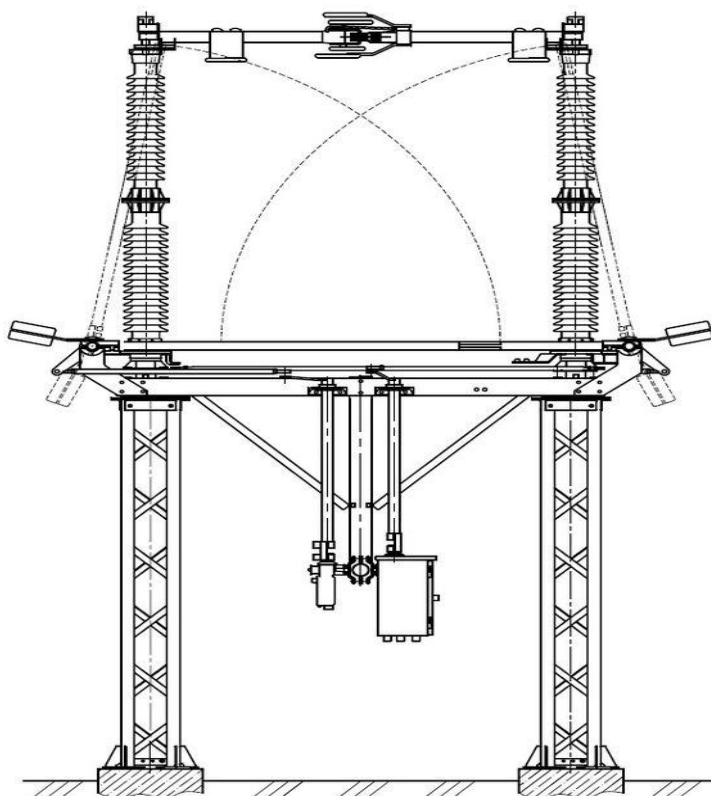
Разъединитель типа РГН-110/1000УХЛ1
